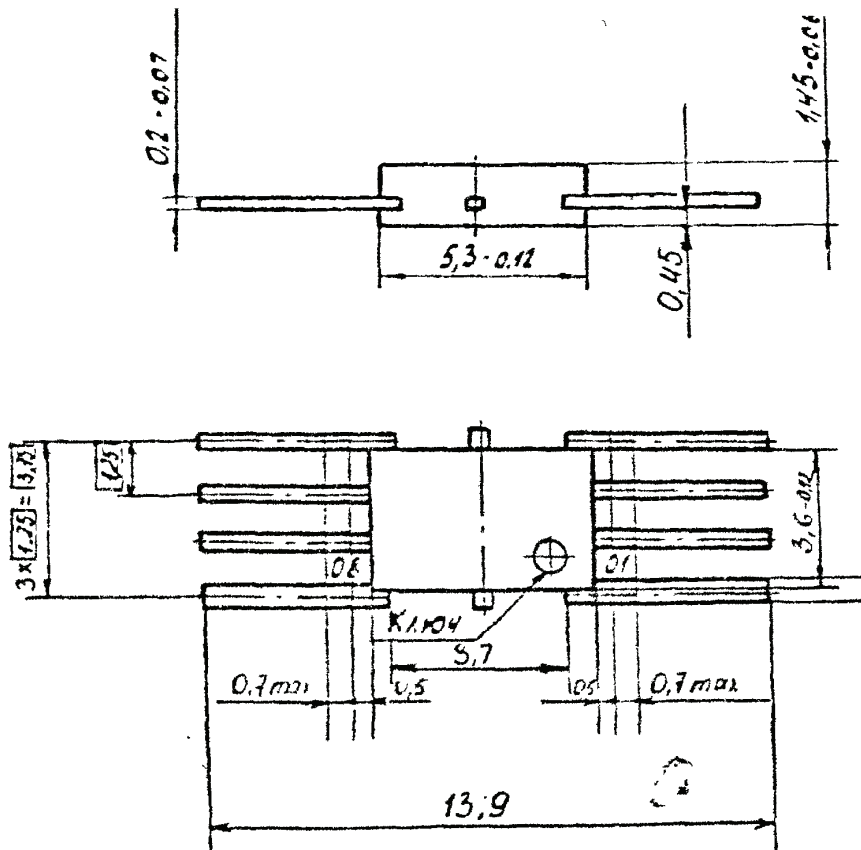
Габаритный чертеж корпуса 4103.8-1
